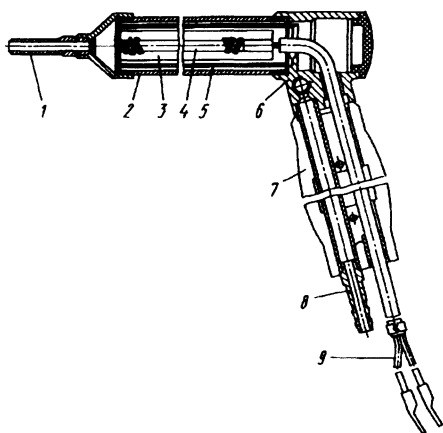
Нагреватель ГЭП-2 для сварки пластмасс:
